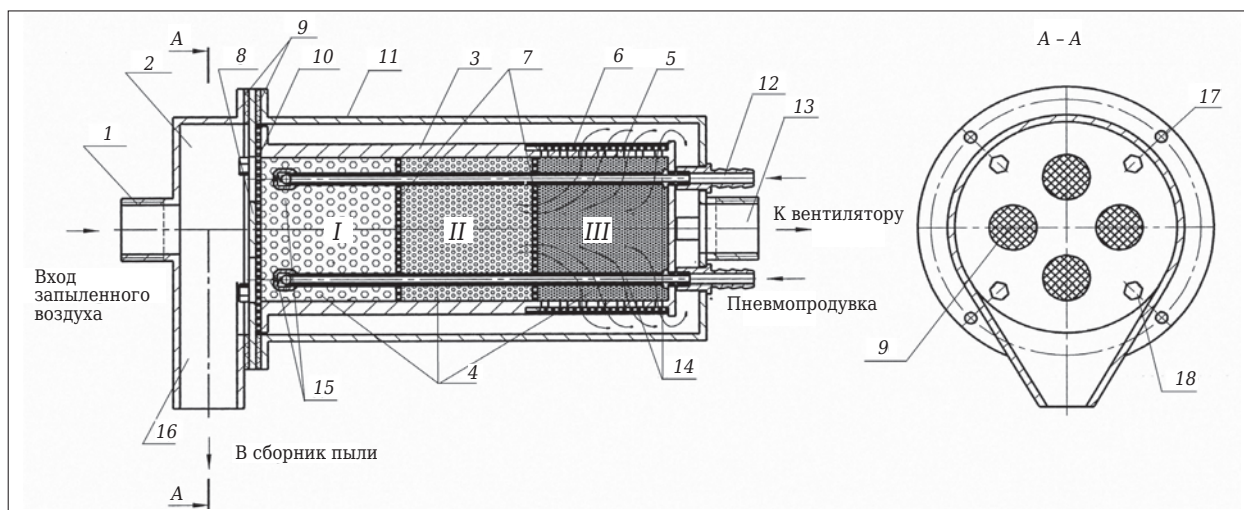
Насыпной комбинированный фильтр: 8 — распределительное устройство; 9 — металлическая решетка; 10 — резиновая уплотнительная прокладка; 11 — корпус фильтра; 12 — штуцеры для регенирующего агента; 13 — коллектор очищенного воздуха; 14 — регенирующие патрубки (дополнительные передвижные коммуникации для импульсной регенерации зернистых слоев); 15 — пружинные клапаны; 16 — патрубок сбора уловленной пыли; 17, 18 — крепежные болты; остальные обозначения — в тексте
